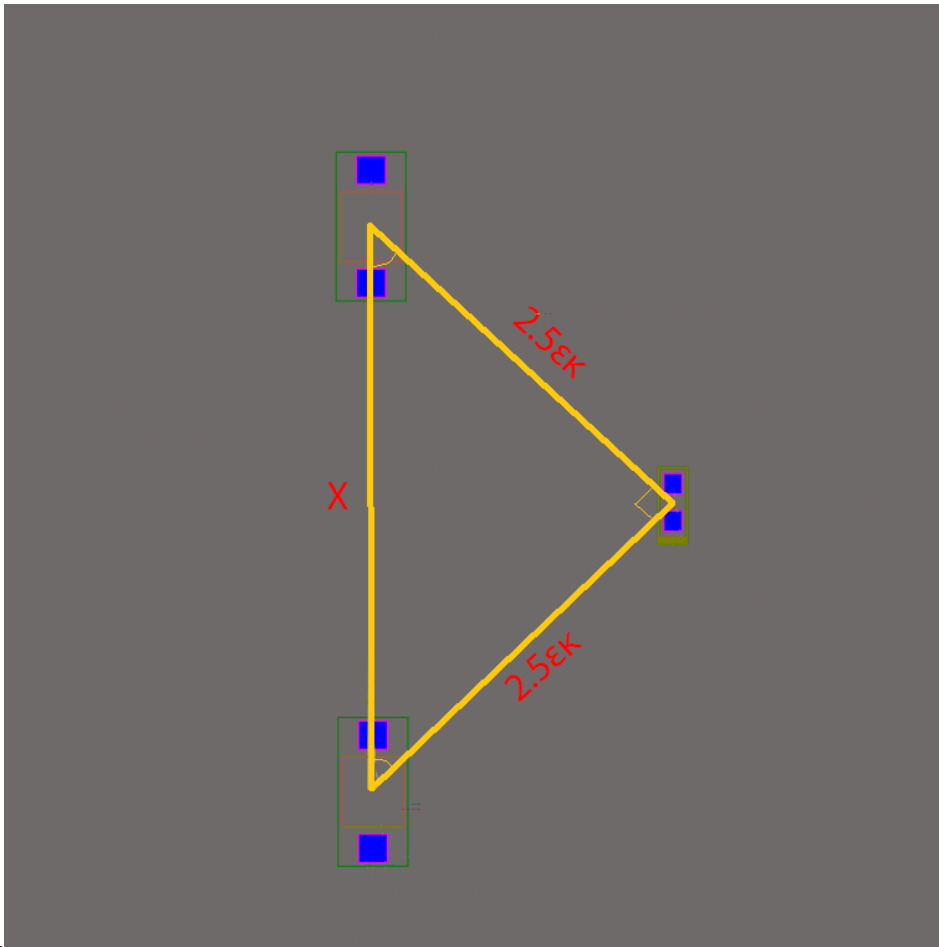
(β) Μέγεθος ύψους της πλακέτας PCB
